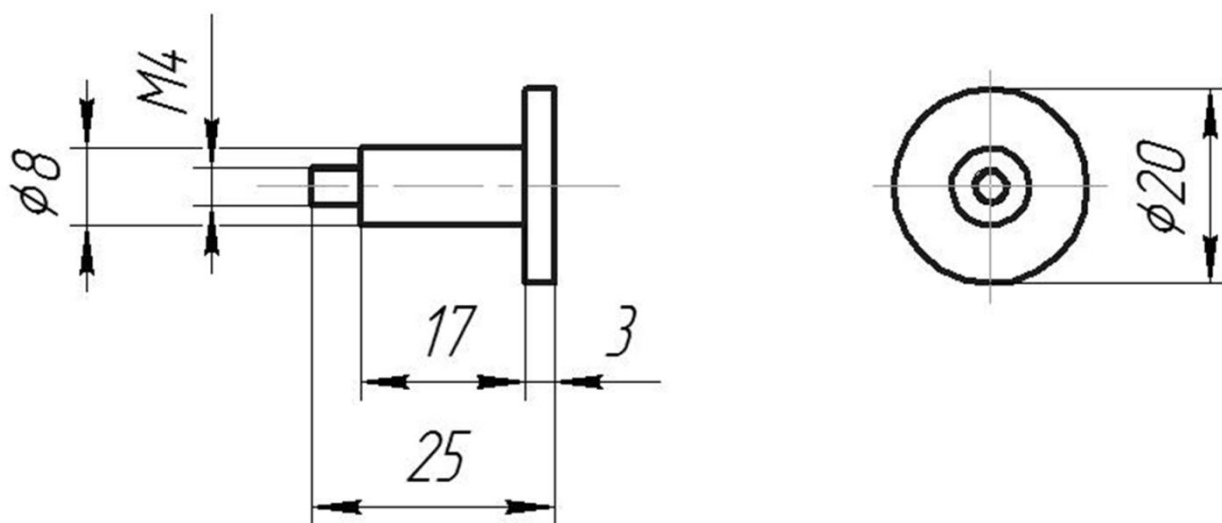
Габаритные размеры ручки для выемки блока
